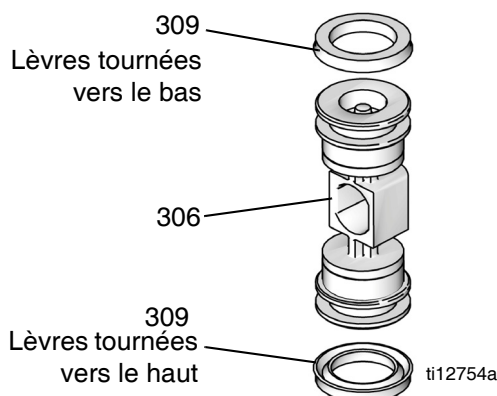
Installation des joints en coupelle de la vanne d'air
